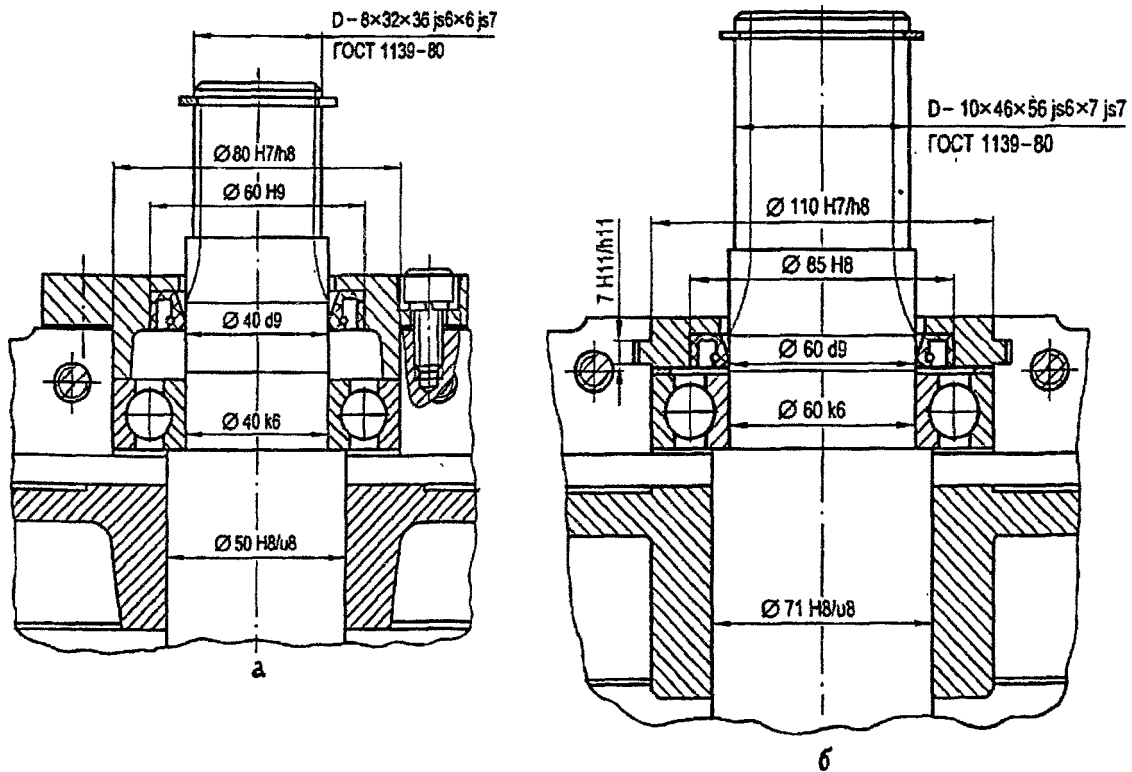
Примеры конструкций подшипниковых узлов с привертными (а) и закладными (б) крышками подшипников
